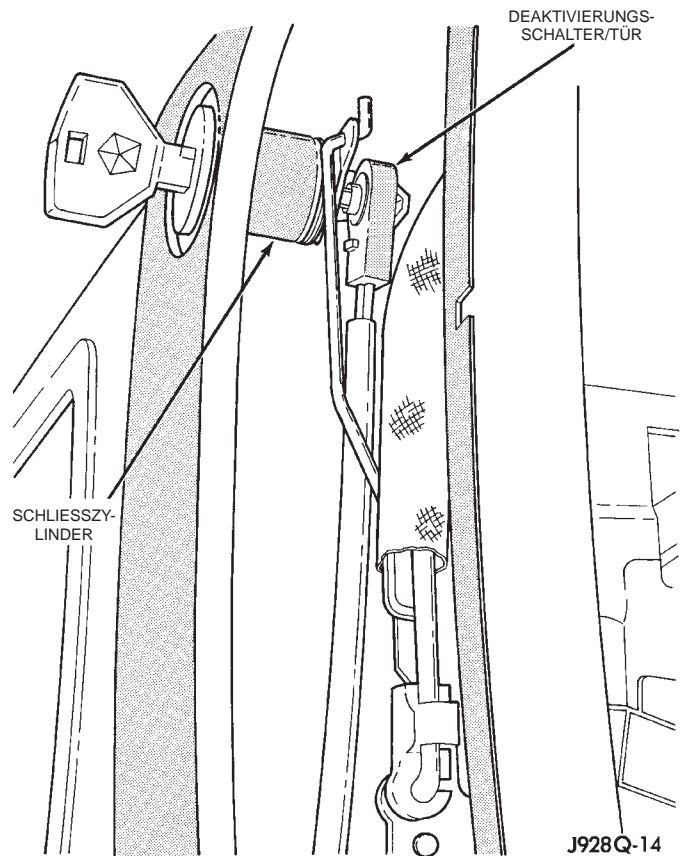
Schalter/Türschließzylinder aus- und einbauen - Typisch
